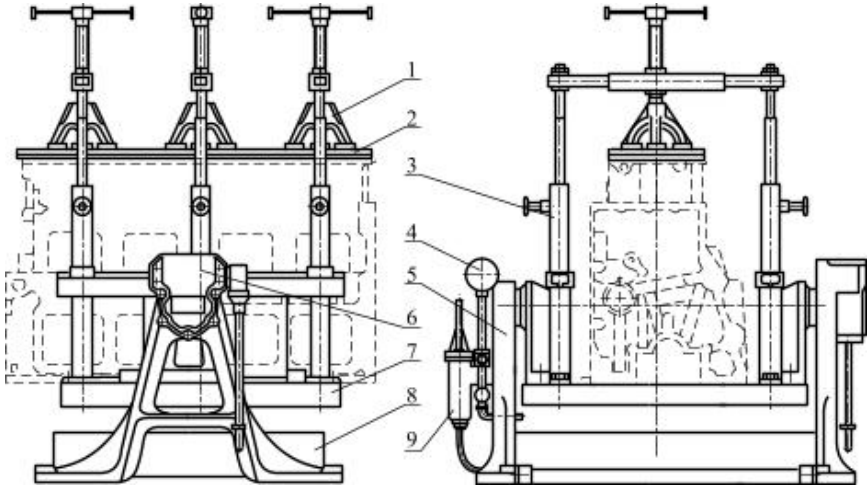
Схема станда для гідравлічного випробування блока циліндрів двигуна: 1 – затискач; 2 – плита; 3 – стійка; 4 – манометр; 5 – опора; 6 – поворотний механізми; 7 – стіл; 8 – ванна; 9 – поршневий насос
